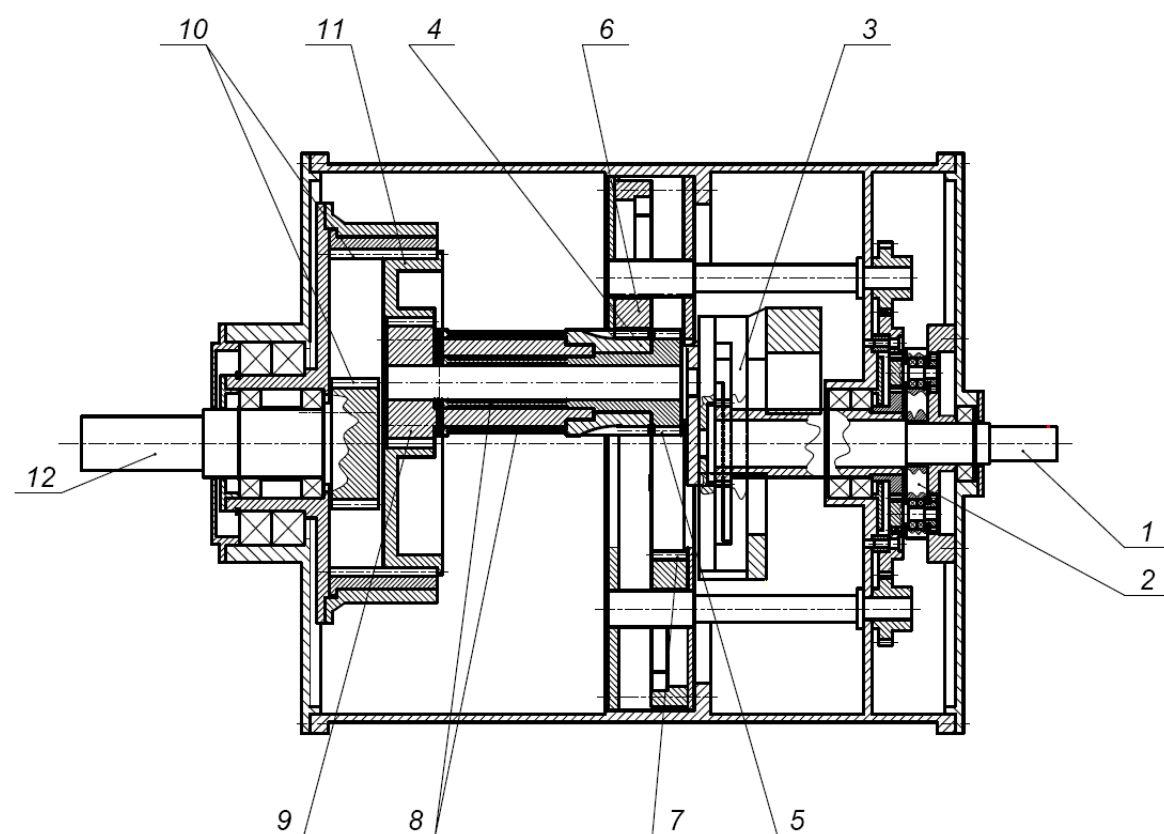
Компонновка планетарной плавнорегулируемой передачи по схеме 1: 1 – ведущий вал, 2 – механизм регулирования передаточного отношения; 3 – механизм балансировки сателлита; 4 – зубчатый венец сателлита первого силового потока; 5 – зубчатый венец сателлита второго силового потока; 6 – сектор центрального зубчатого колеса первого силового потока; 7 – сектор центрального зубчатого колеса второго силового потока; 8 – трубчатые торсионы; 9 – дополнительный зубчатый венец сателлита; 10 – планетарная передача съема вращения с сателлита; 11 – опорная вставка; 12 – выходной вал
